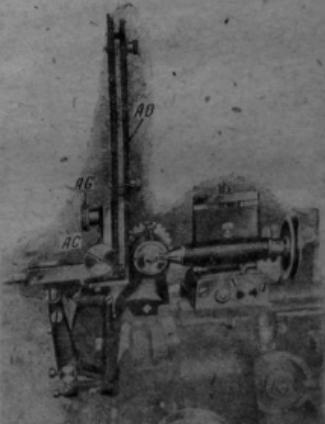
Станок Петерман для фрезеровки торцовых зубьев. Делительное устройство и шпиндель.
